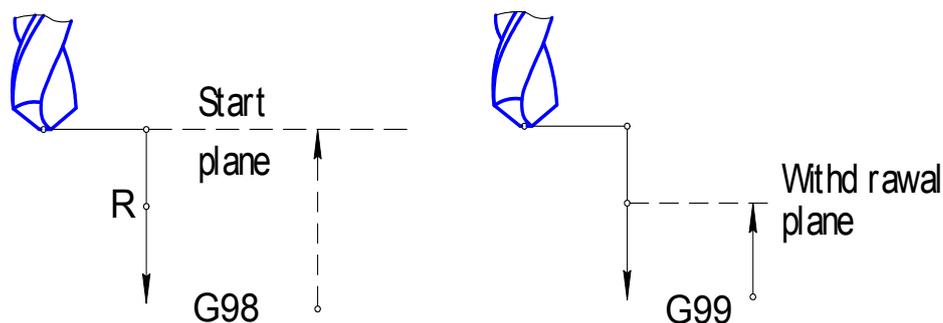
Движения инструмента при G81 - цикл сверления
